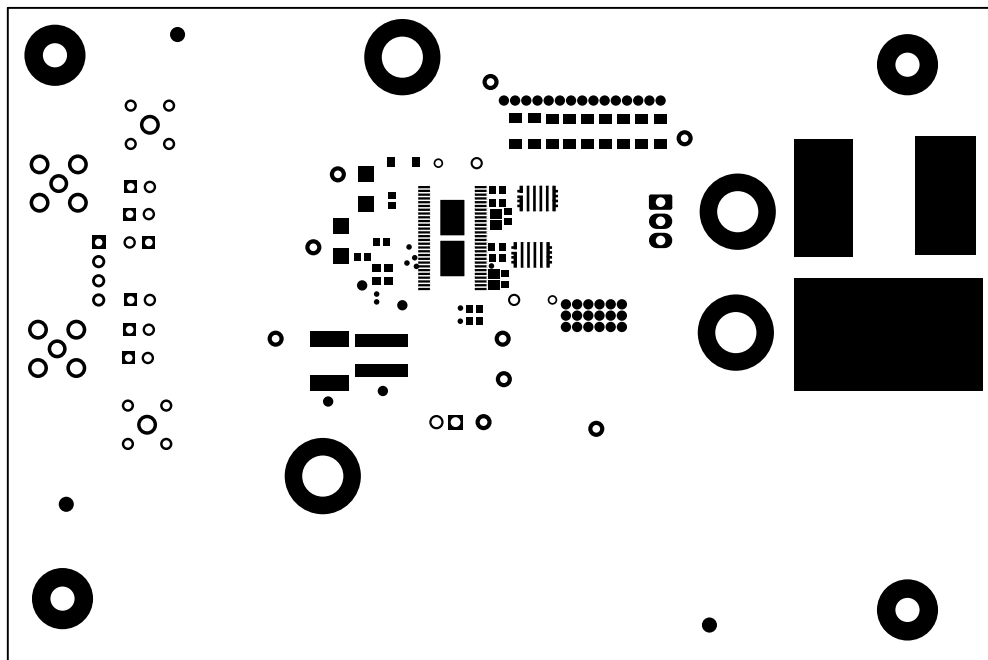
顶部焊锡层 (TPS7H6005EVM)
